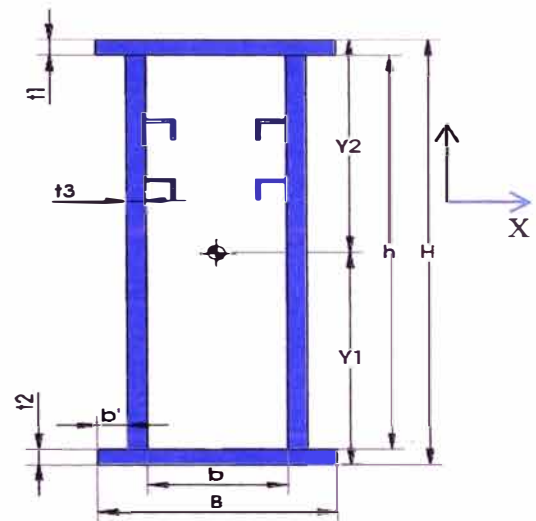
Perfil de viga cajón para FEM 4m
